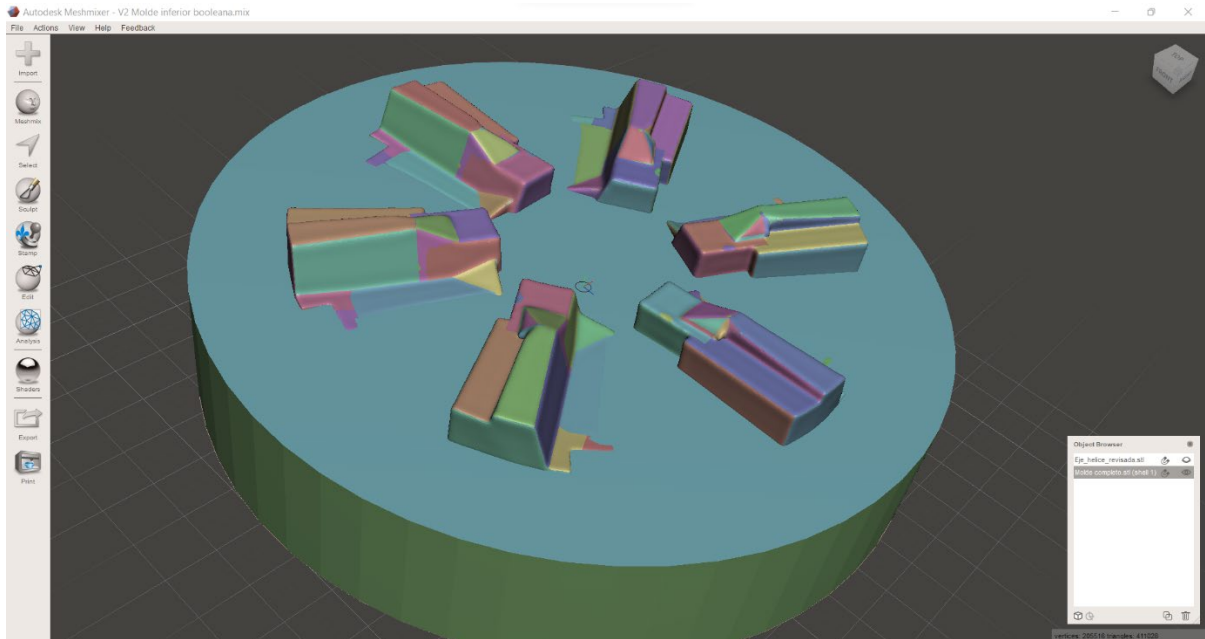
Unión booleana de la parte inferior del molde con el desnivel entre pala de la hélice.
